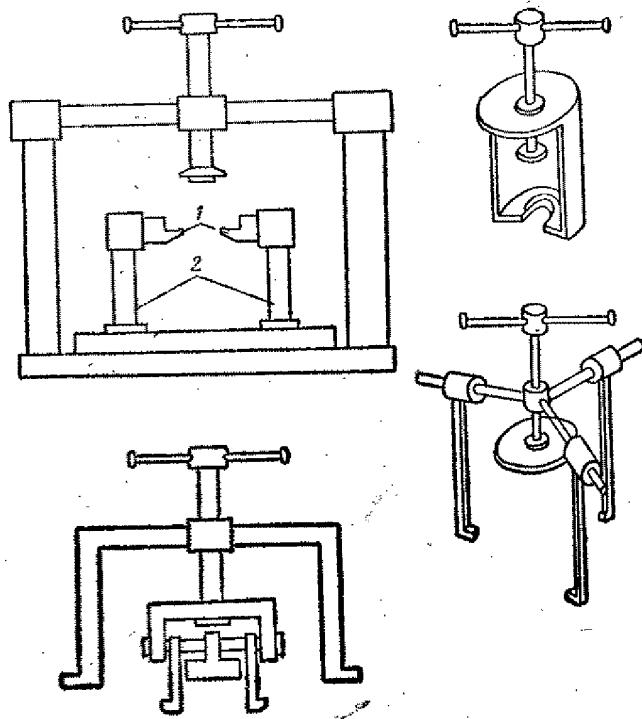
Схемы типовых приспособлений для демонтажа подшипников:
